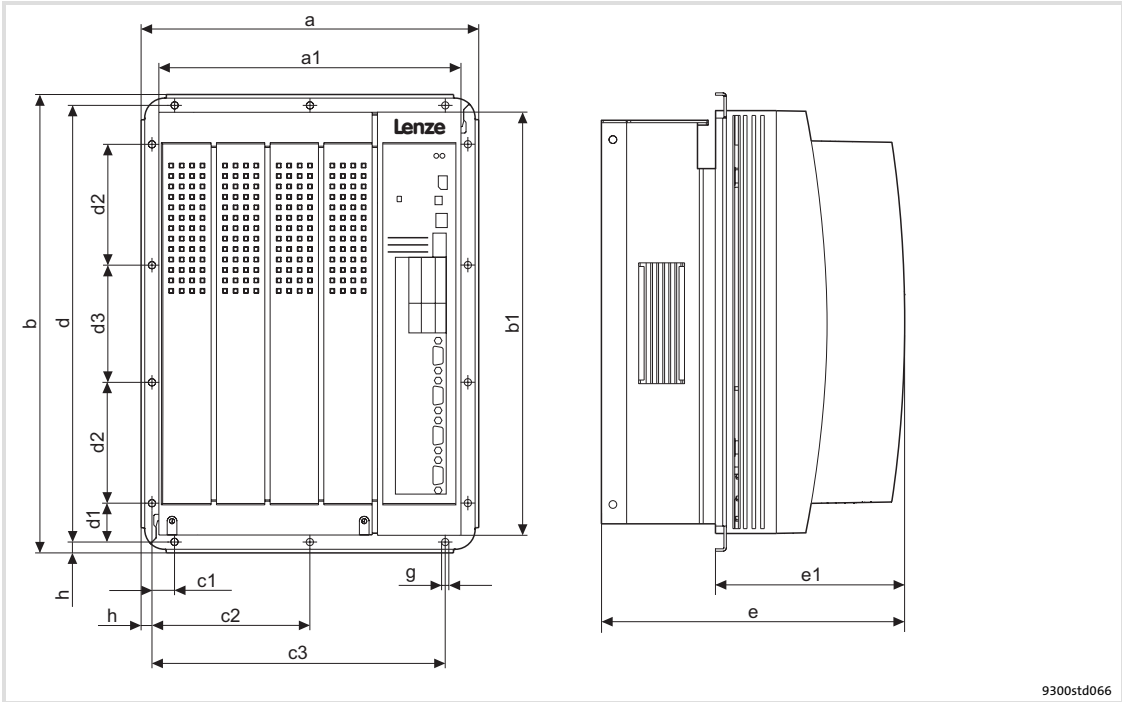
Abmessungen Montage thermisch separiert 15 ... 30 kW
